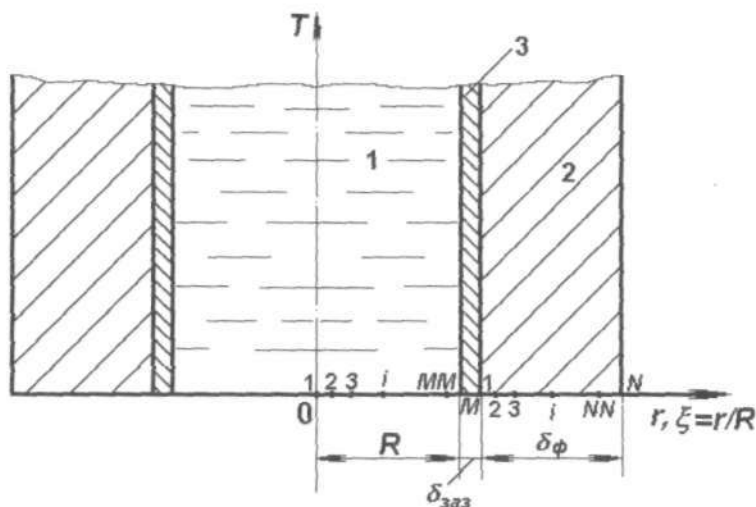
Схема отливки, затвердевающей в литейной форме:
